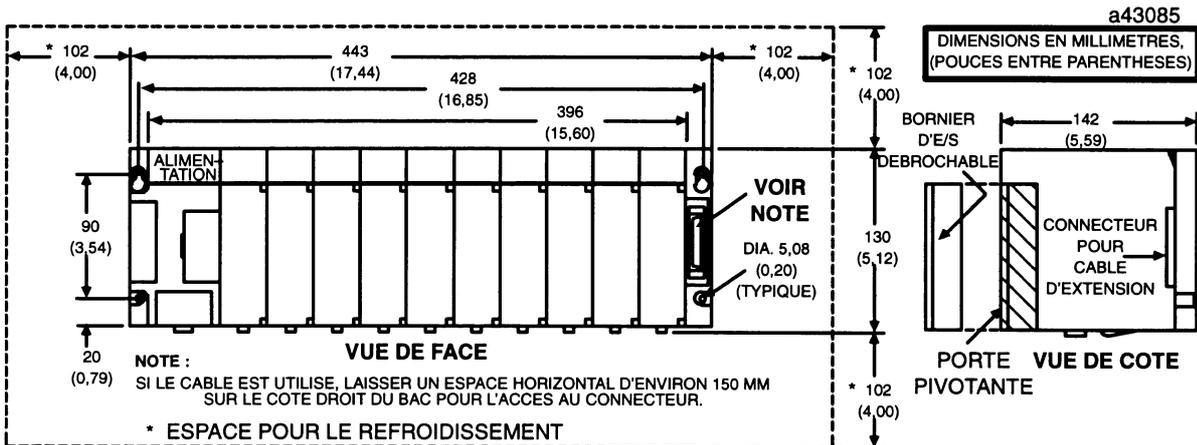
Dimensions de montage et espace nécessaire pour les platines à 10 emplacements modèles 331, 340 et 341
